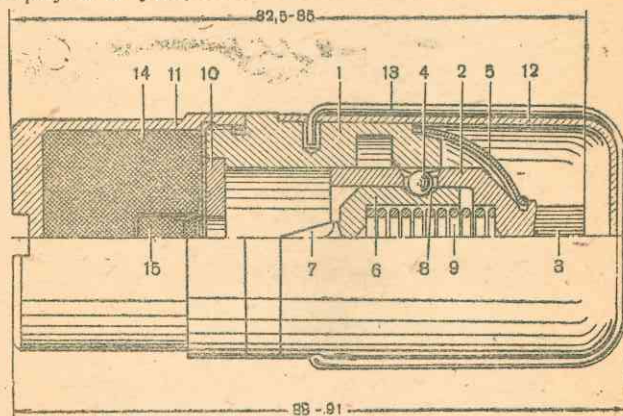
Взрыватель МВ-3 к мине ПМЗ-40:
